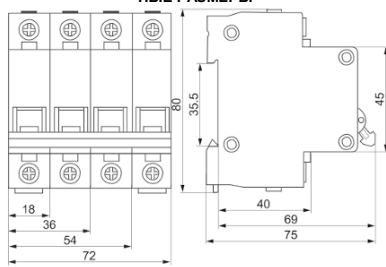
Габаритные, установочные, присоединительные размеры выключателей
